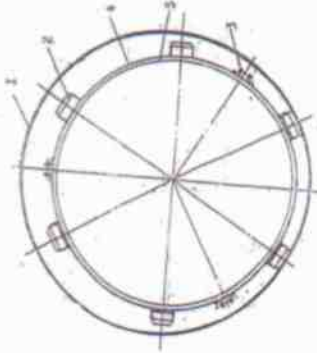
Опорно-направляющее кольцо. - кожух; - изолялектрический опорный элемент; - болтовое соединение сегментов; - сегмент опорного кольца; - прокладка
